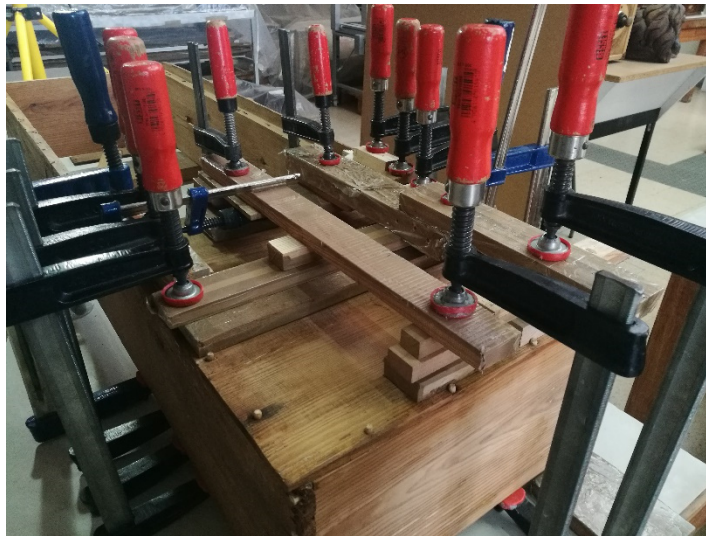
Montagem dos vários elementos que constituem o fundo do gavetão (colagem e cavilhamento). Fonte: própria
